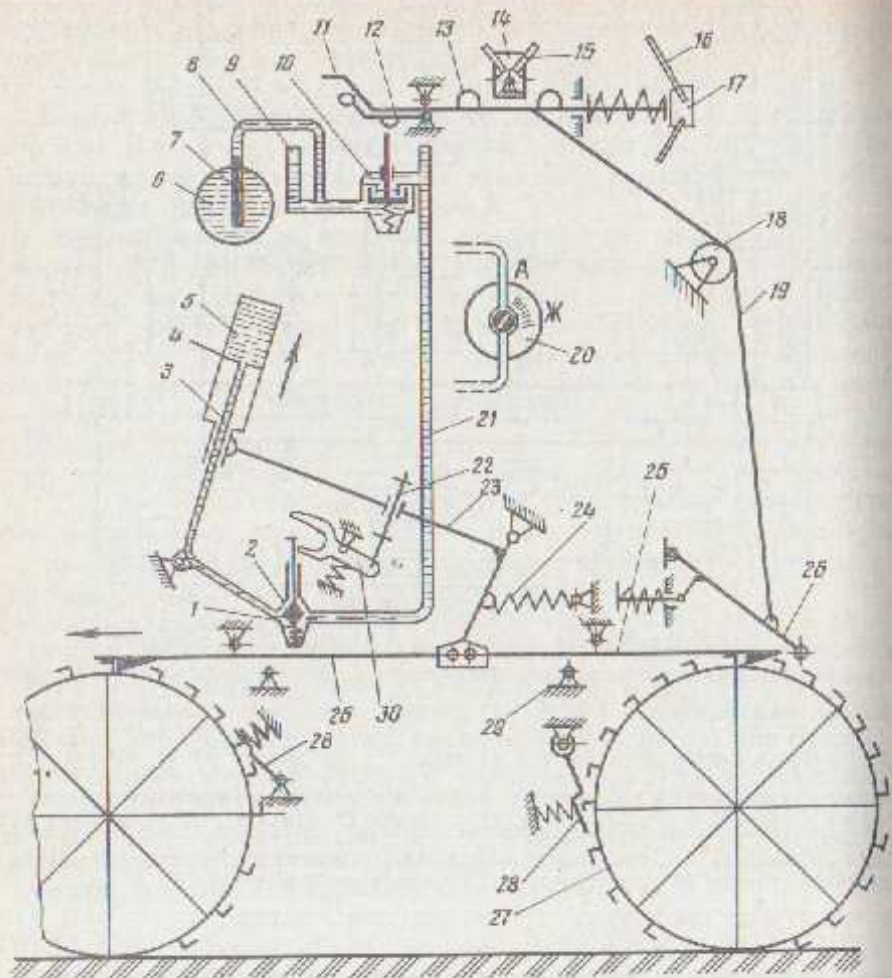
Схема гидропривода и механического тормоза тележки машины «Фрегат»:
